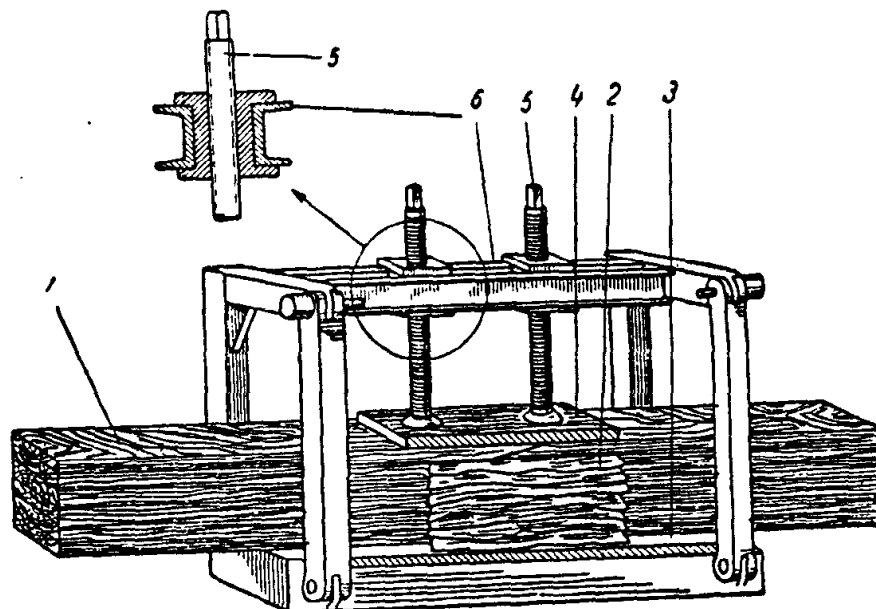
Пневматический пресс для склейки заготовок по толщине.
